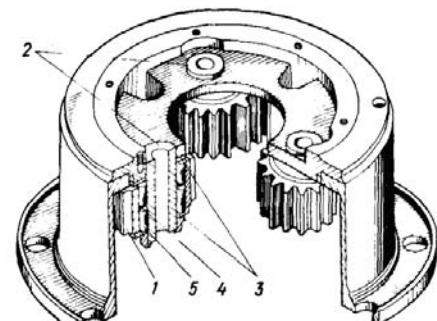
Разборка водила: 1 — сателлит; 2 — палец; 3, 4 — шайба; 5 — ролик
